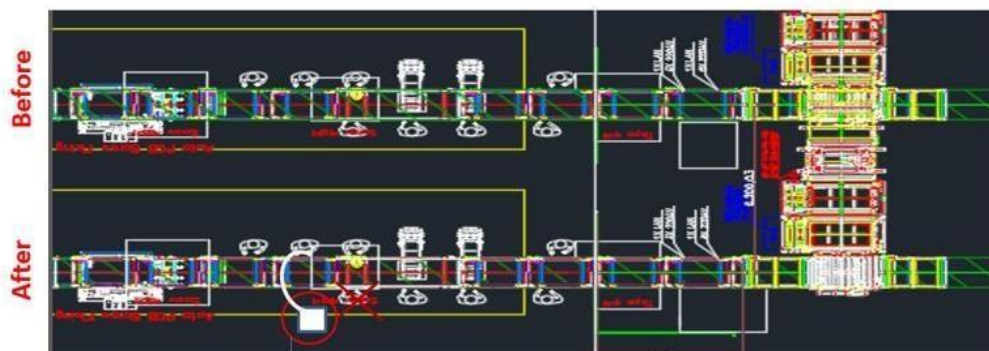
Layout da Máquina. Fonte: O Autor (2023)
